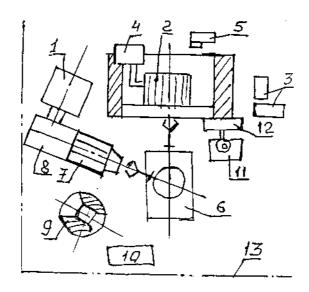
Типовая структурная схема РТК горячей объемной штамповки из штучной заготовки:
